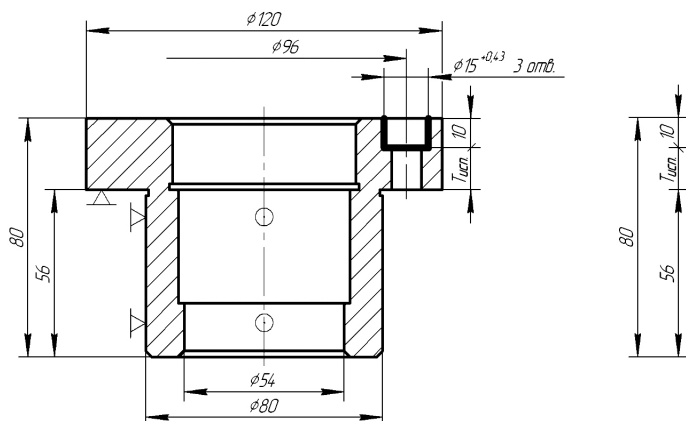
Операционный эскиз обработки и размерная цепь в случае базирования по ступице диаметром 120 и цилиндрической поверхности диаметром 80
